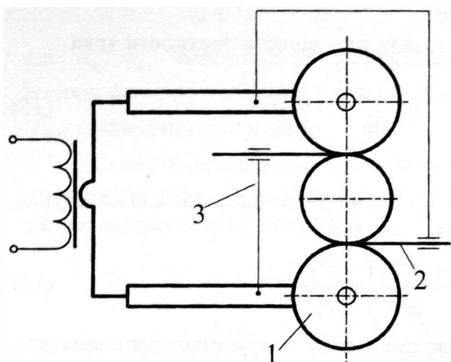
Схема включения привариваемых проволок в сварочную цепь:
